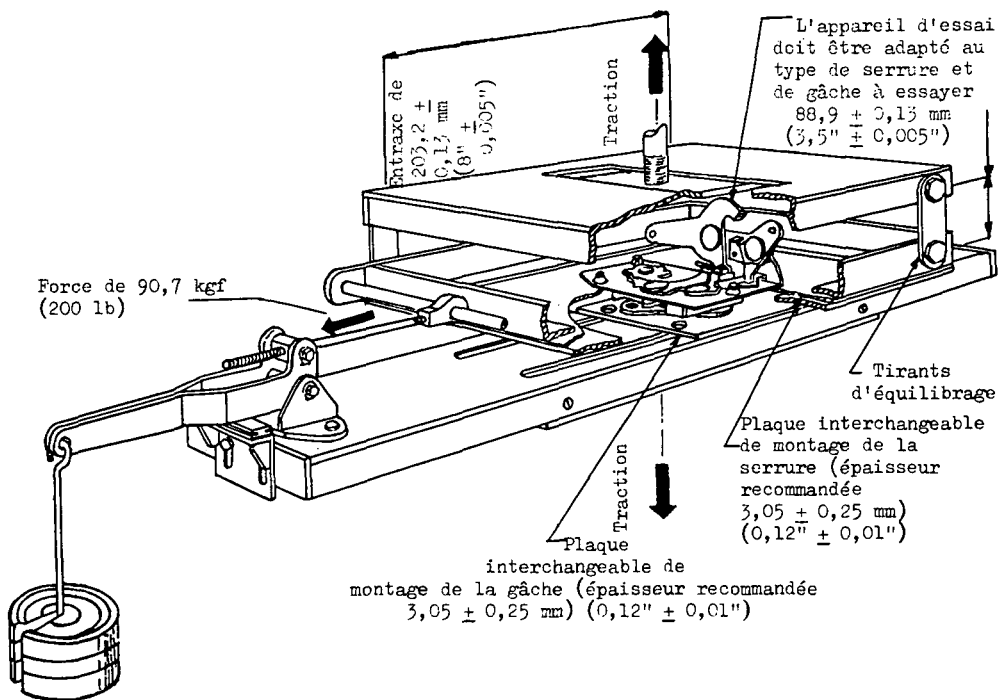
SERRURES DE PORTES — DISPOSITIF D'ESSAI DE CHARGE STATIQUE (CHARGE TRANSVERSALE)
